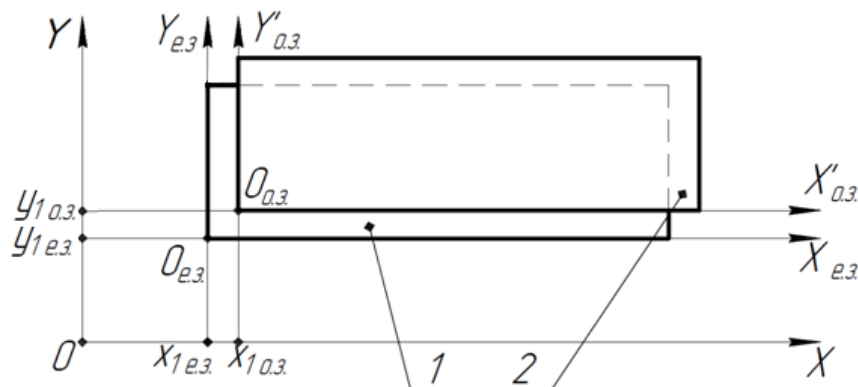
Суміщене зображення дійсного положення еталонної заготовки та корегованого положення оброблюваної заготовки відносно осей системи координат верстата в горизонтальній площині XU
